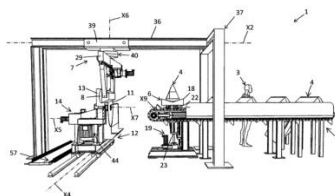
brevet « Machine de dressage de merrains » - FR3078499
